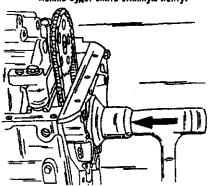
Запрессовка сальника коленчатого вала со стороны привода газораспределительного механизма.
